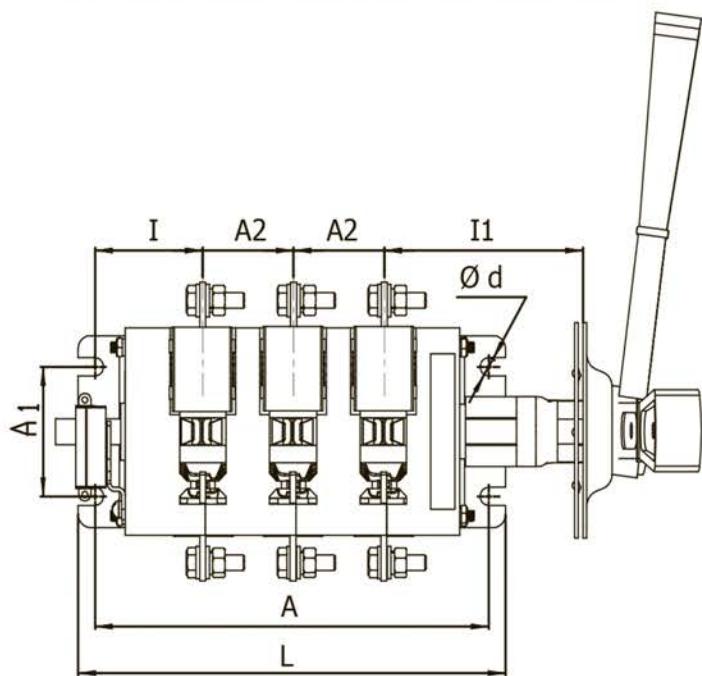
Выключатель-разъединитель трехполюсный на одно направление с боковой смещенной рукояткой.
